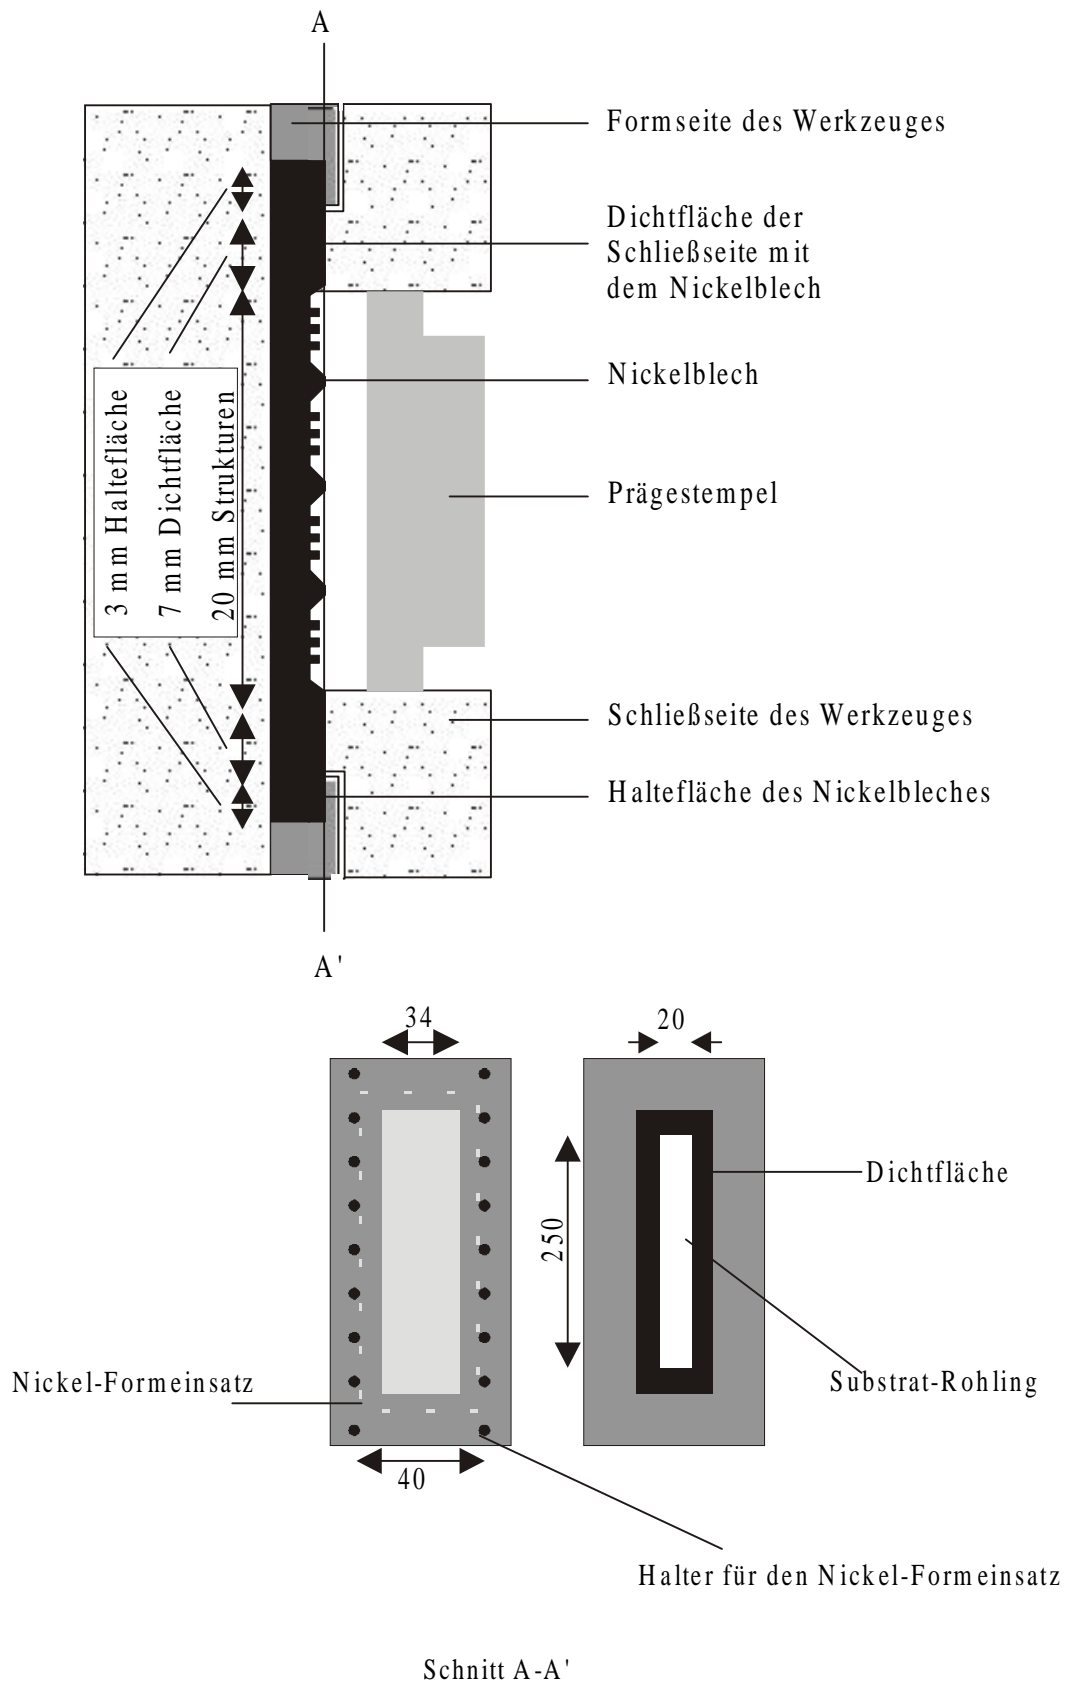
Prinzip des Heißprägewerkzeuges, große Kavität [Mün]
